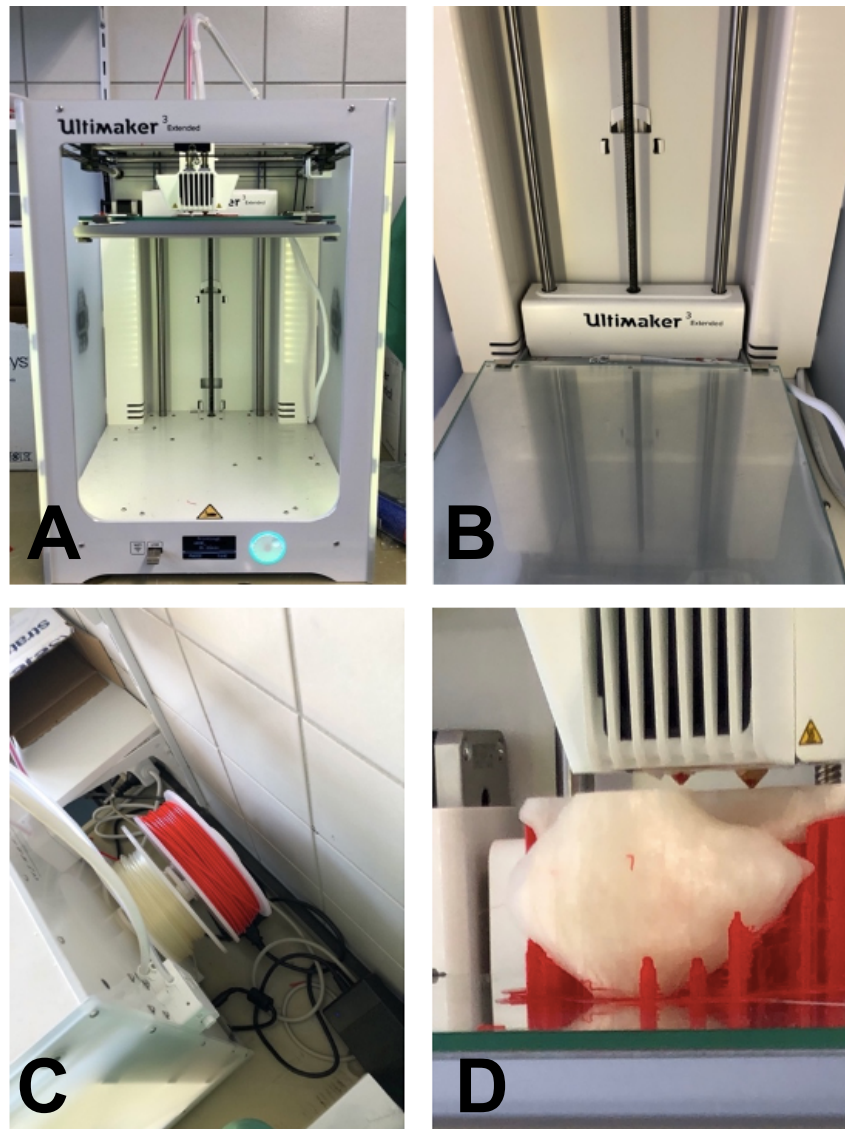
(A) 3D Drucker UltiMaker® 3 Extended der Firma UltiMaker®; (B) Build Plate aus Glas; (C) Dualer Extruder - mit rotem und weißem Filament; (D) Modell während des Druckvorgangs
